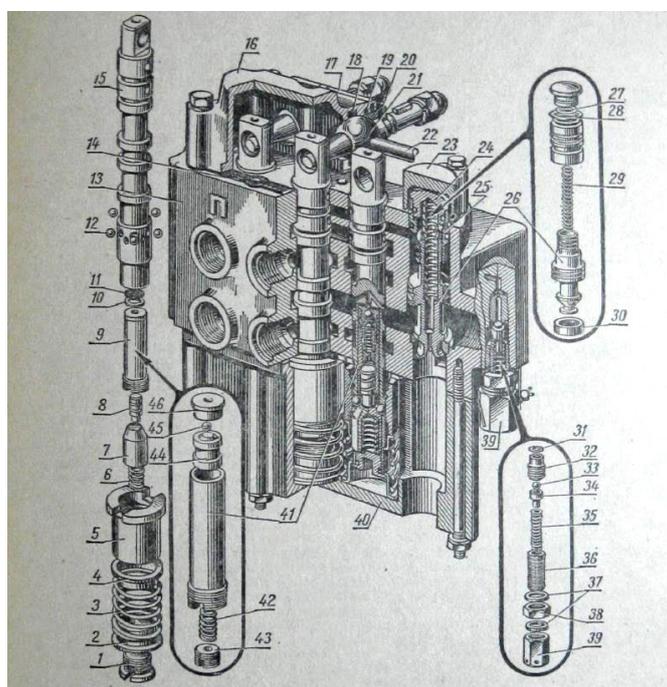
Распределитель Р75-В3: 1-Пробка; 2-нижняя тарелка; 3-пружина автомат; 4-верхняя тарелка; 6-пружина втулки фиксатора; 7-втулка фиксатора; 8-бустер; 9, 41-гильзы; 10 и 14-прокладки; 11-фильтр; 12-шарик фиксатора; 13-корпус распределителя; 15-золотник; 16-верняя крышка; 17-планка; 18 и 27-уплотнительное кольцо; 19-пыльник; 20-пылезащитная манжета; 21-рычаг; 22-ось рычагов; 23-упор; 24-пробка перепускного клапана; 25-направляющая перепускного клапана; 26-перепускной клапан; 28-стопорное кольцо; 29-пружина перепускного клапана; 30-седло перепускного клапана; 31 и 37-уплотнительные шайбы; 32-гнездо предохранительного клапана; 33-шарик; 34-направляющая предохранительного клапана; 35-пружина предохранительного клапана; 36 и 43 регулировочные винты; 38-контргайка; 39-колпачок; 40 - нижняя крышка; 42 - пружина клапана автомата; 44-направляющая клапана автомата; 45-шариковый клапан; 46-гнездо клапана автомата
